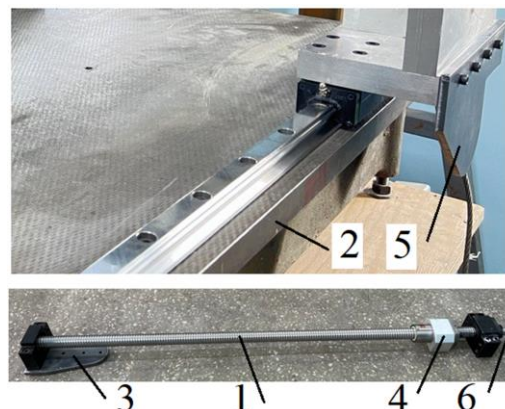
Механизм перемещения портала фрезерного 3 – D станка по оси X.
